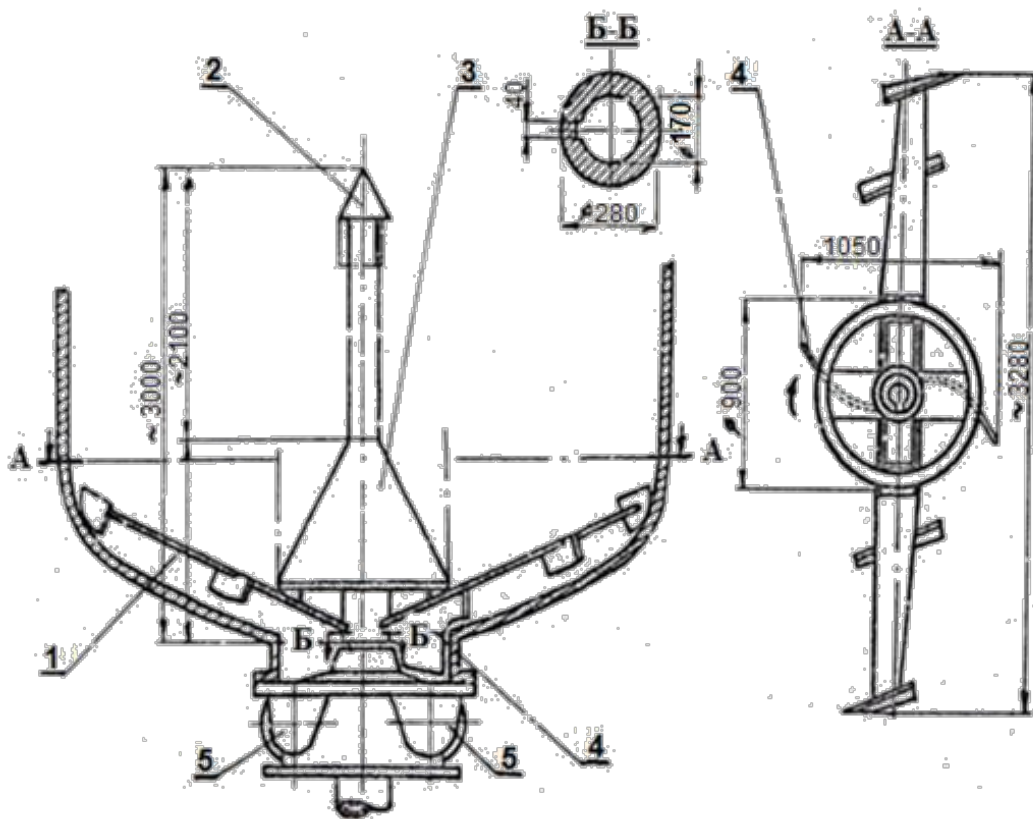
Разгрузочное устройство установки непрерывной варки целлюлозы «Камюр»:
